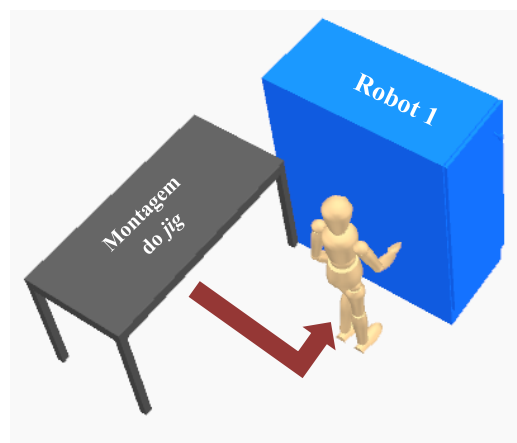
Entrada do *jig* no *robot* 1 (soldadura das redes às bobinas) após a montagem.
